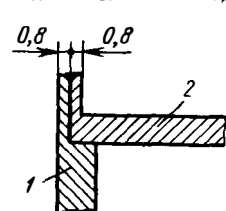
Вариант конструкции регенерируемого сварного шва:
